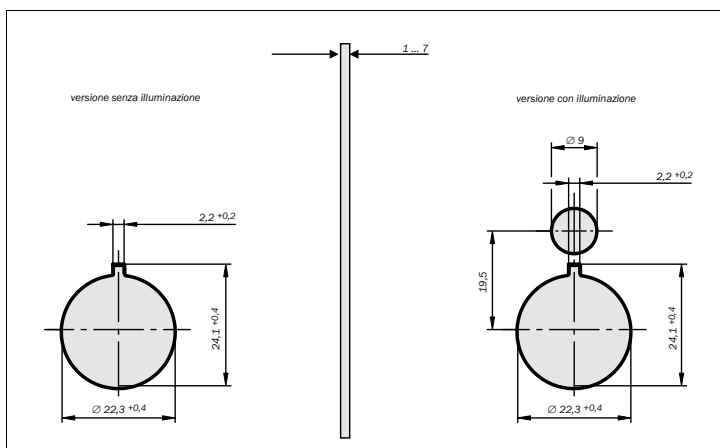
disegni quotati dei fori di montaggio per le versioni a incasso (mm)
